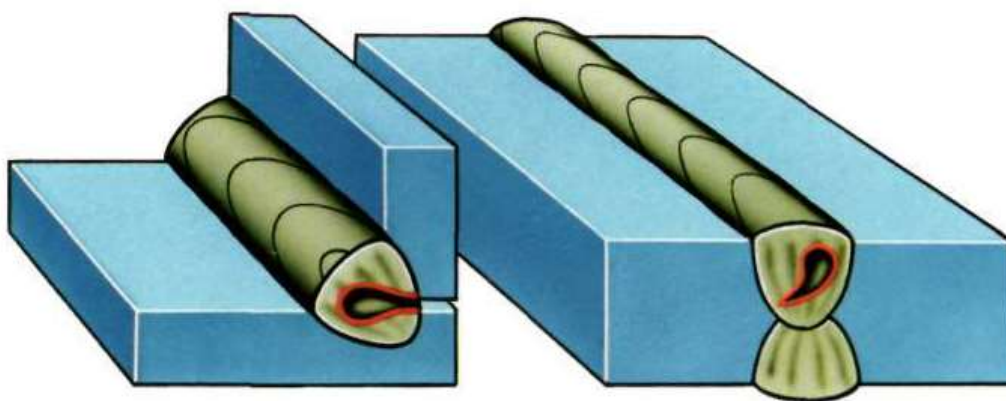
Дефекты сварного шва по типу свища
